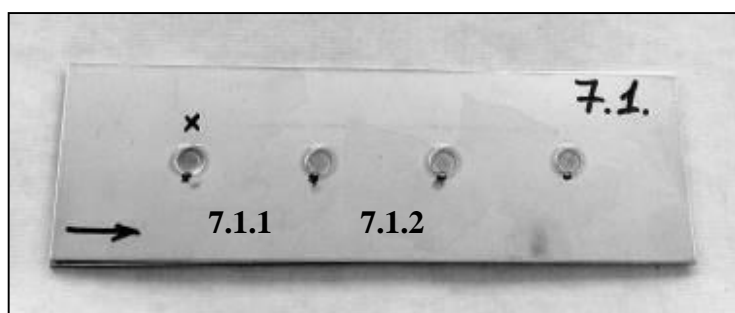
Внешний вид точечной контактной сварки образца № 7.1
